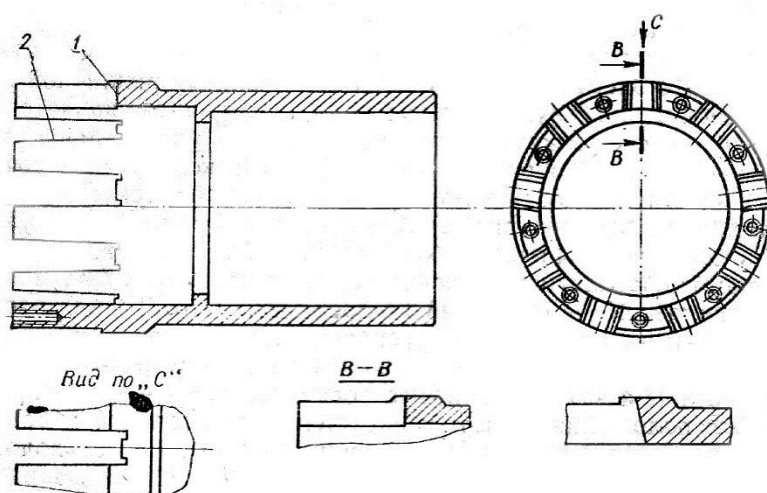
Корпус сепаратора: 1 – корпус сепаратора; 2 – бічні поверхні пазу
